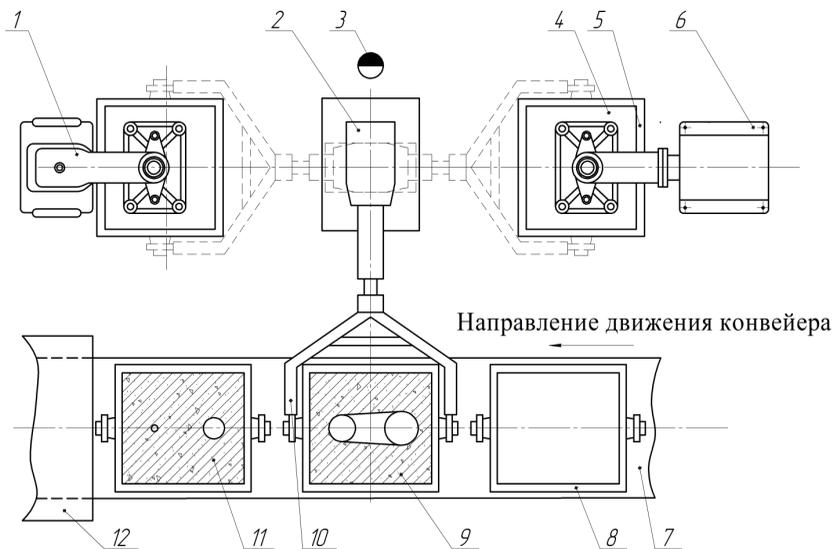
Роботизированный комплекс машинной формовки: 1 – формовочная машина для изготовления верхних полуформ; 2 – ПР; 3 – оператор РТК; 4 – приемные ролики; 5 – формовочная машина для изготовления нижних полуформ; 6 – поворотное устройство; 7 – конвейер; 8 – пустая опока; 9 – нижняя полуформа; 10 – захватное устройство ПР; 11 – верхняя полуформа; 12 – маркировщик
